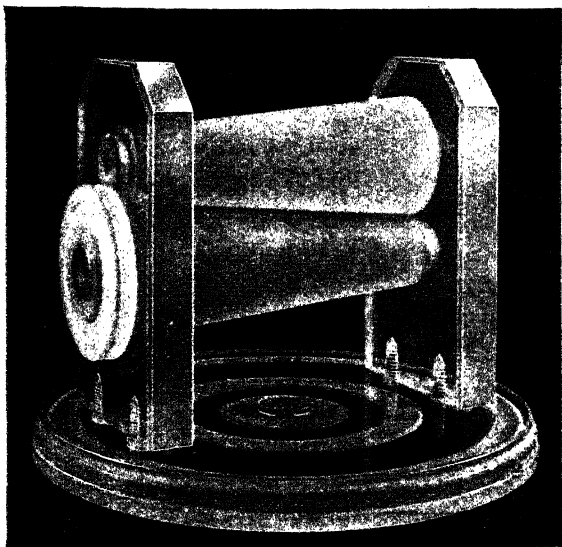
Kalender aus Glas, bearbeitet mit Hartmetallwerkzeugen.
